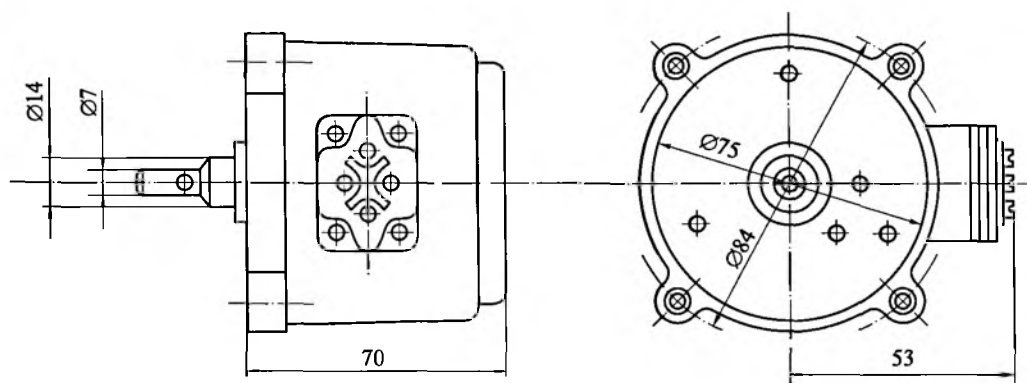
Габаритные и установочно-присоединительные размеры исполнительного асинхронного редукторного двигателя РД-09
